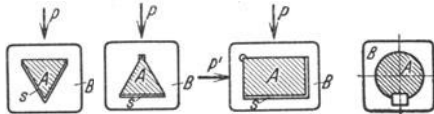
bis 4. Ausführungsformen gerader Führungen. (A feste Führung, B beweglicher Schlitten, S Spiel.)
